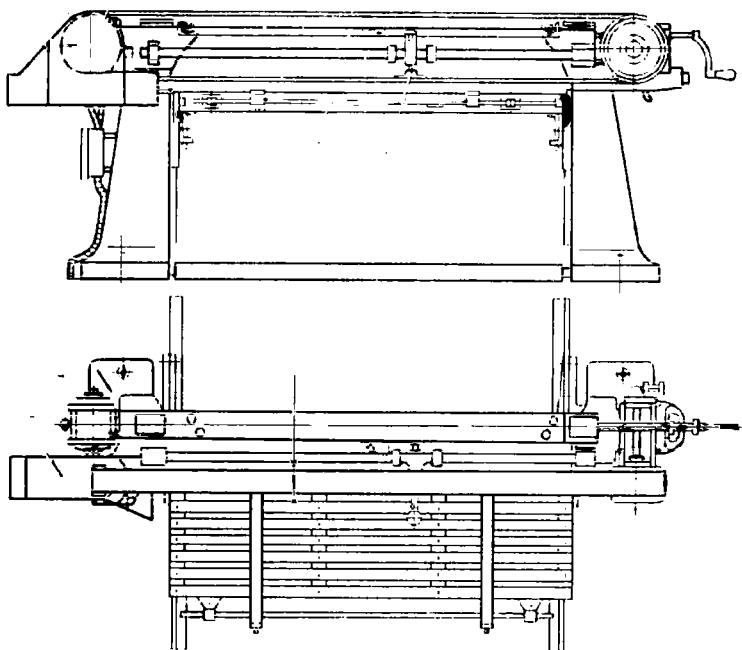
Схема шлифовального ленточного станка ШЛПС-7:
